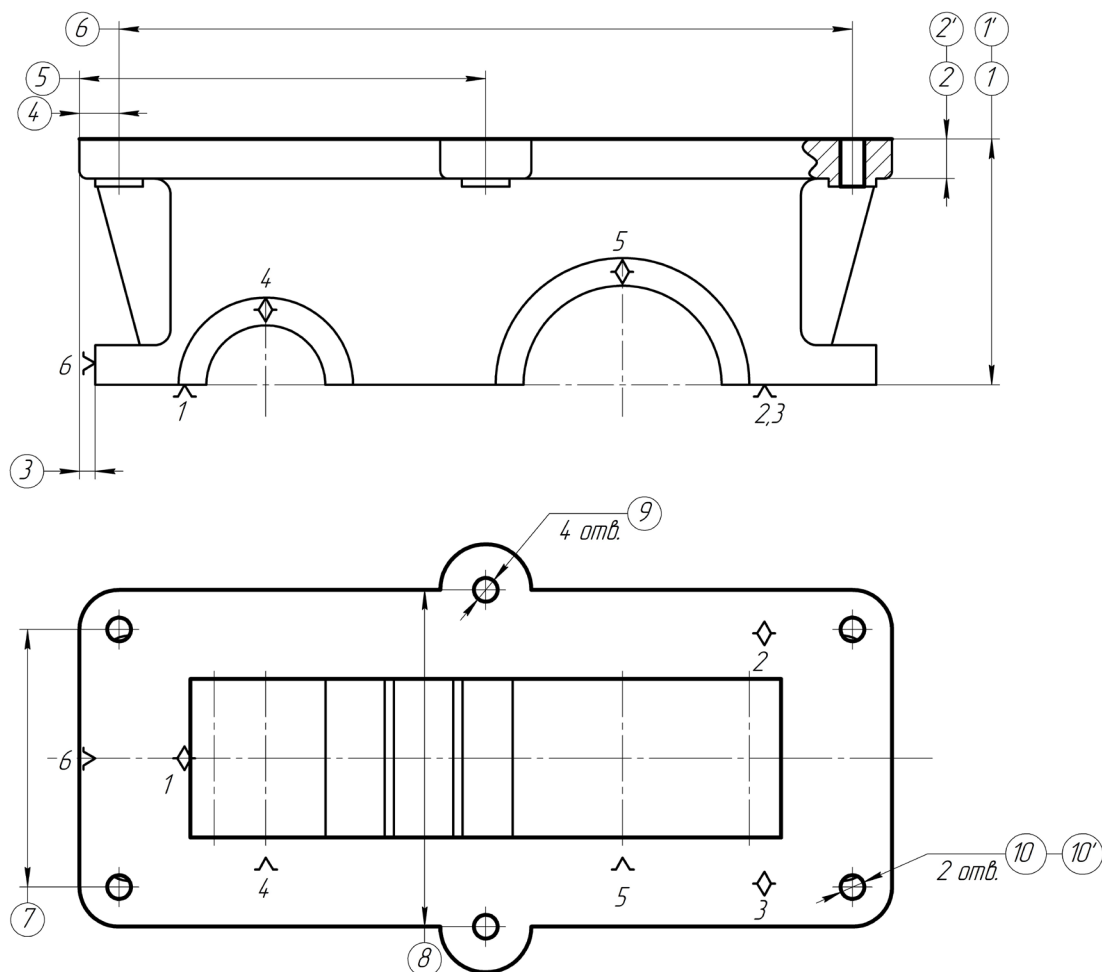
Операційний ескіз оброблення деталі для операції 005
